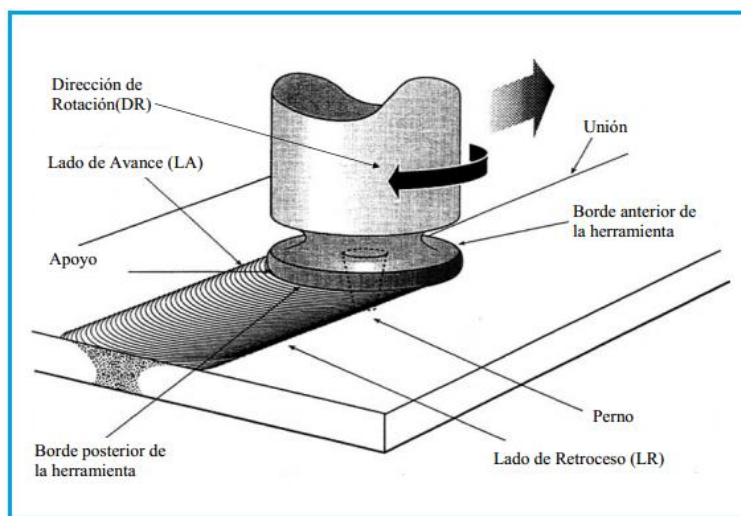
Proceso de soldadura por fricción.
